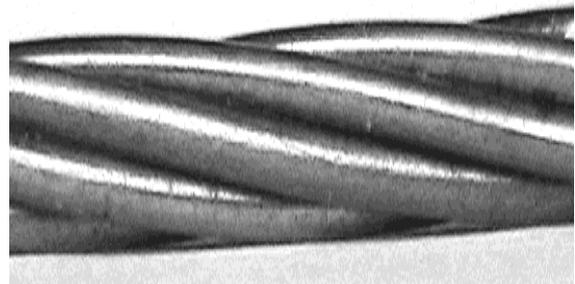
Образец № 2 спиральной свивки диаметром 2,4 мм изготовленный с равномерным натяжением проволок
